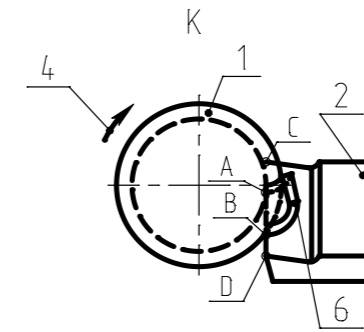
Взаимное положение резца и заготовки (вид К)
